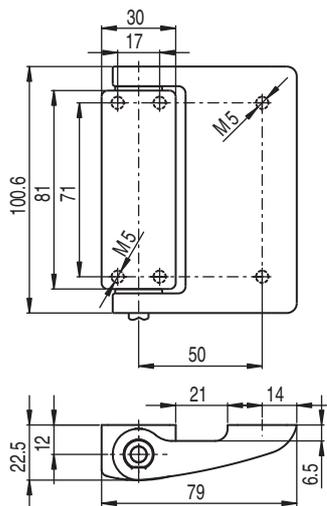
Dimensions du S410-M1CB2-B en mm
